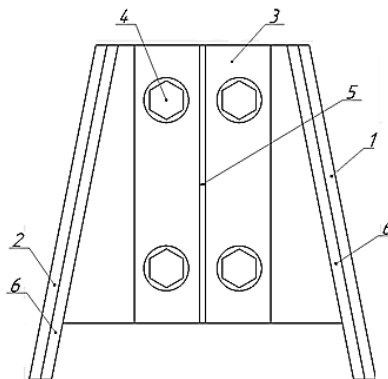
Комбинированный режущий сегмент для конусообразного рабочего органа измельчителя кормов вид сверху
